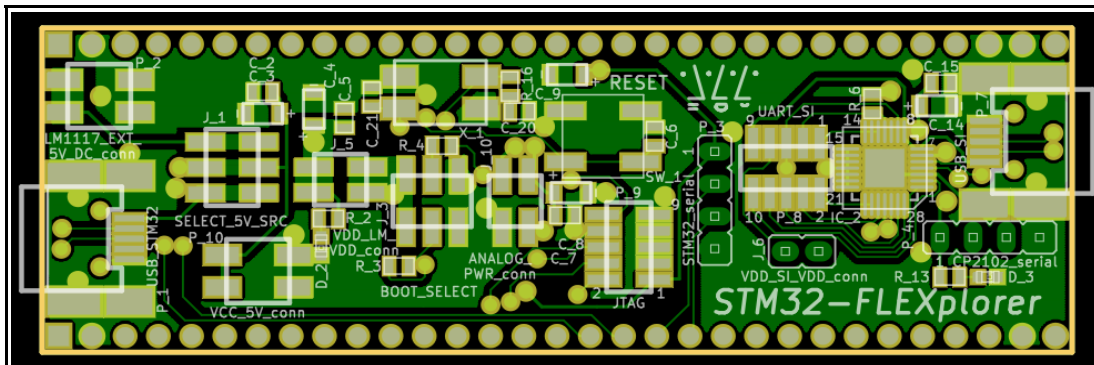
Frontansicht des fertigen Platinen-Layouts
